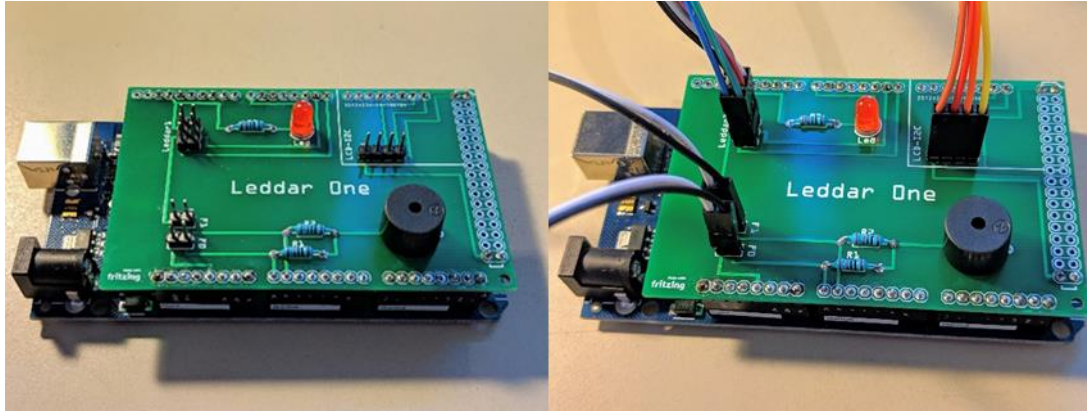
Placa PCB montada sobre la placa de Arduino y con los componentes externos conectados.
